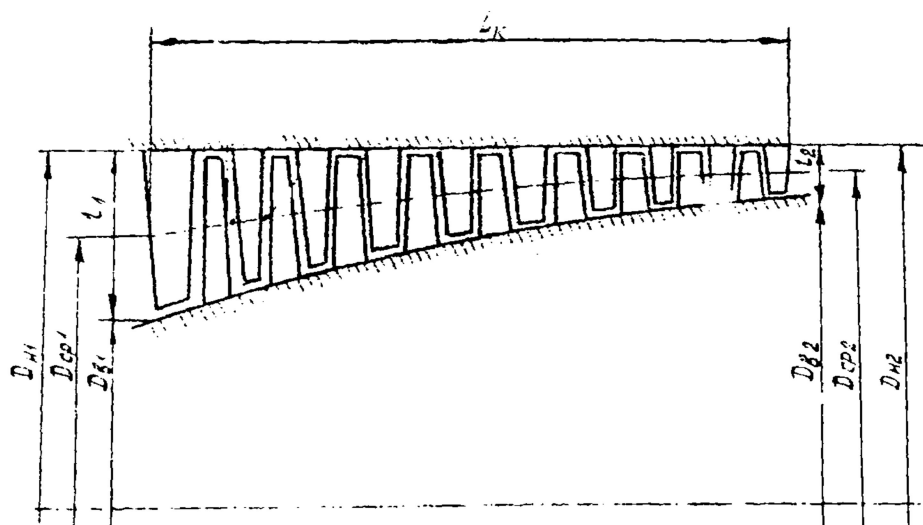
Меридіанний переріз проточної частини компресора ГТД
